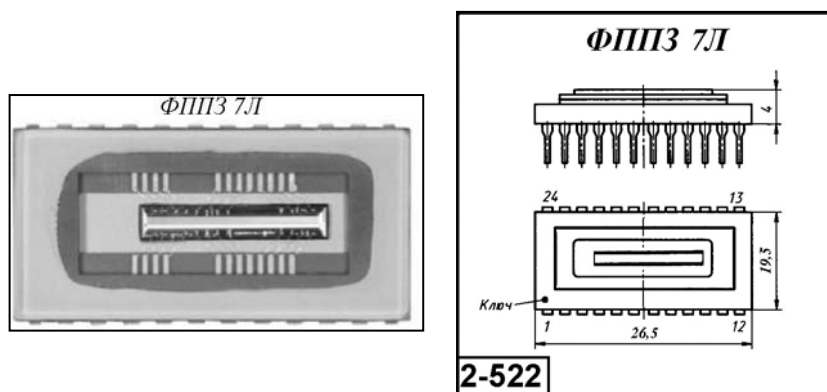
Внешний вид и габаритные размеры ФППЗ 7Л
